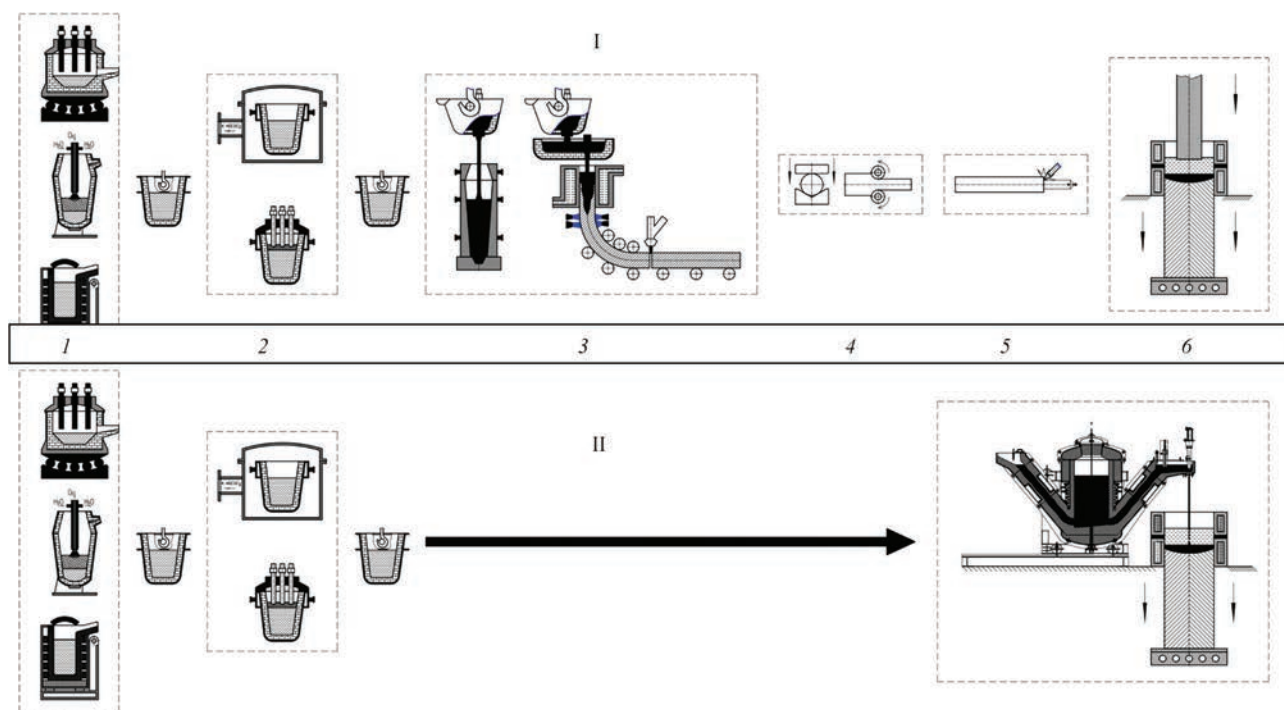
Технологічний ланцюг виготовлення злитків ЕШП з витратними електродами (I) та ЕШП РМ (II): 1 — ДСП, КК, ИП; 2 — позапічна обробка; 3 — розливка в злитки або заготовки МБЛЗ; 4 — деформація заготовки/злитка; 5 — приварювання злитка або катаної/кованої заготовки до інвентарної головки електродотримача; 6 — ЕШП/ЕШП РМ
